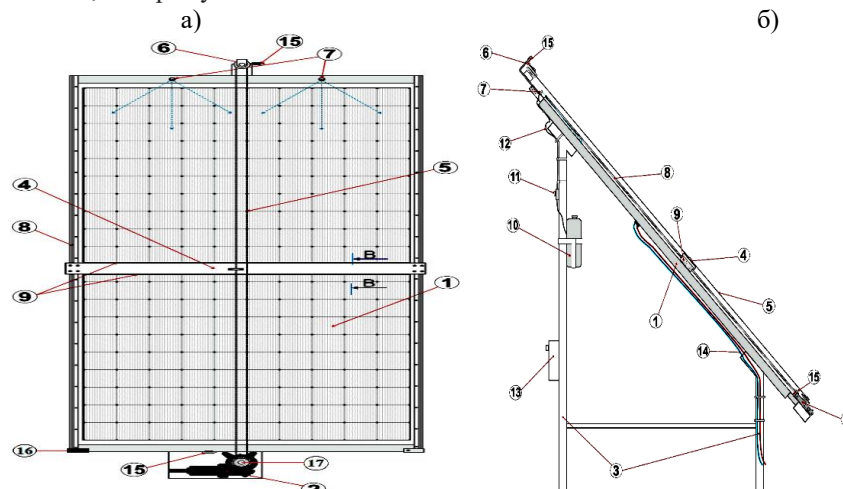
Принципиальная схема устройства очистки: а – вид спереди; б – вид сбоку
